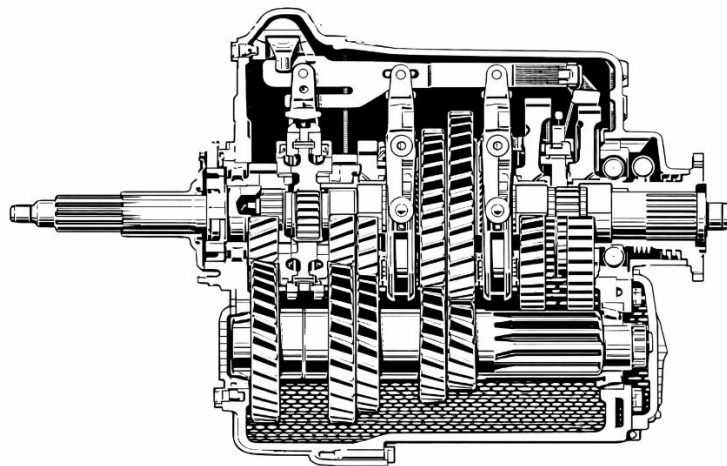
Поздовжній розріз коробки передач G4/GV4
